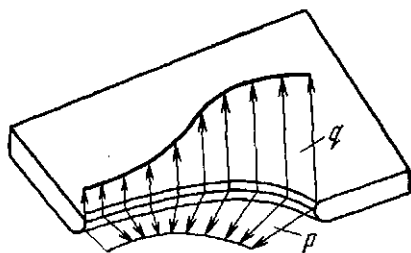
Эпюры распределения давления q и сил растяжения p при затяжке заготовки верха обуви пластинами
